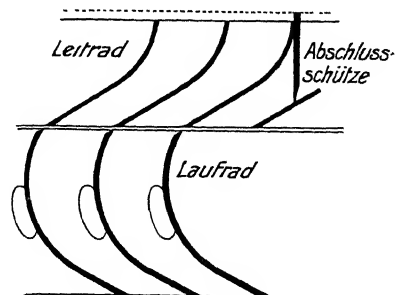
Zylindrischer Schaufelschnitt einer Axialteilturbine.
